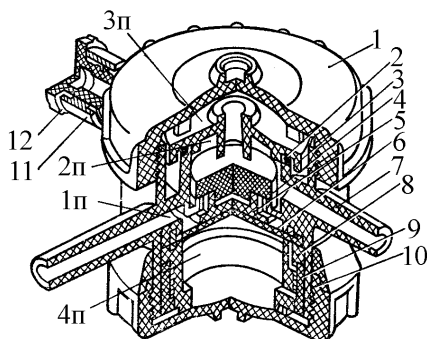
Пульсатор аппарата АДУ-1: 1 – верхняя гайка; 2 – прокладка; 3 – крышка; 4 – клапан; 5 – обойма; 6 – мембрана; 7 – корпус; 8 – камера; 9 – кольцо; 10 – гайка нижняя; 1п – камера постоянного вакуума; 2п, 4п – камеры переменного вакуума; 3п – камера атмосферного давления
